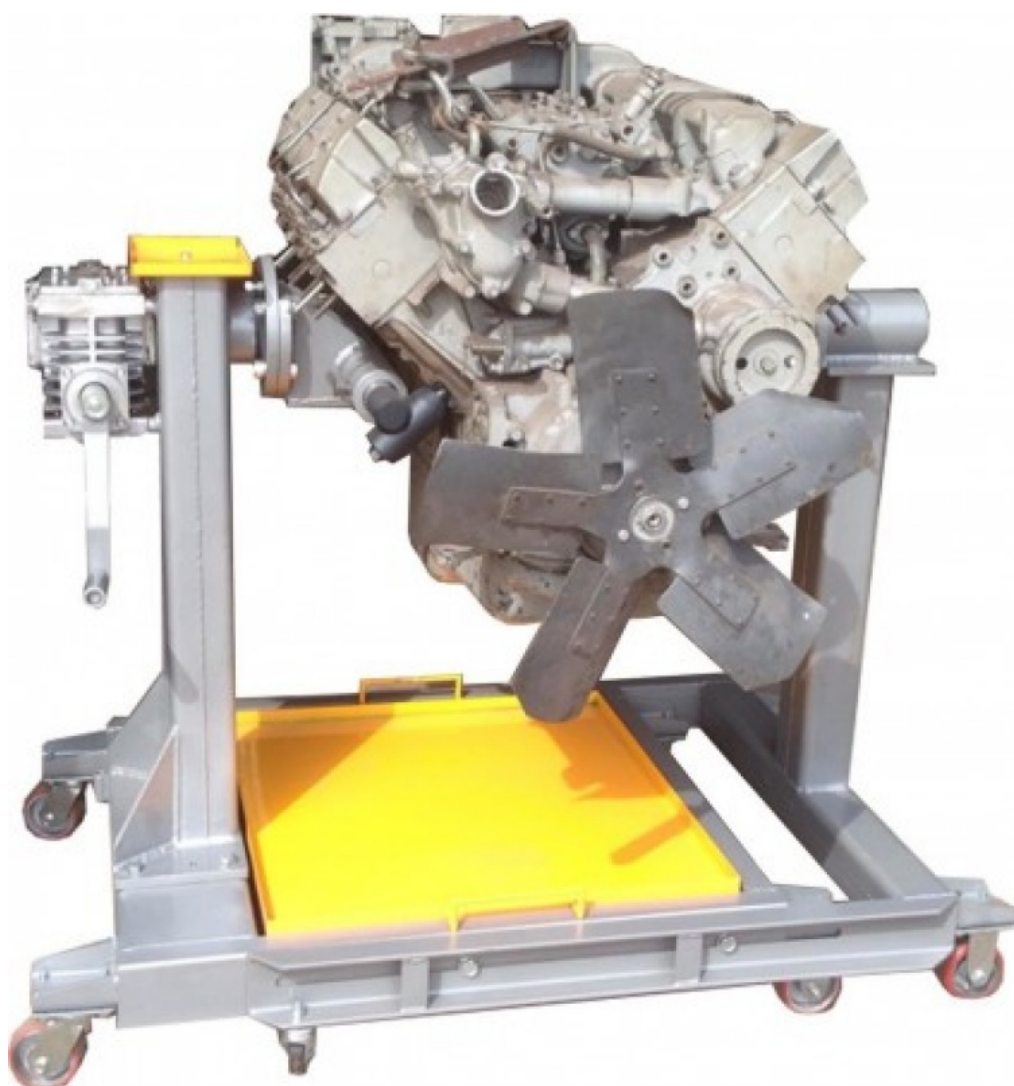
Стенд для сборки двигателя грузового автомобиля СДУ-100
